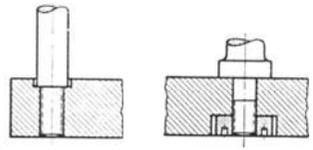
u. 135. Säulenbefestigung durch Gewinde.
